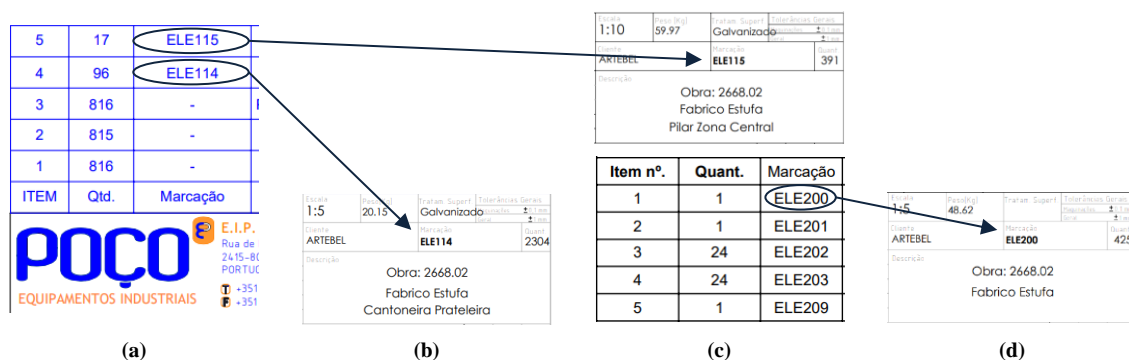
Fluxo de montagem entre desenhos de (a) Montagem; (b) Peça Solta; (c) Conjunto e (d) respetivo Croqui
